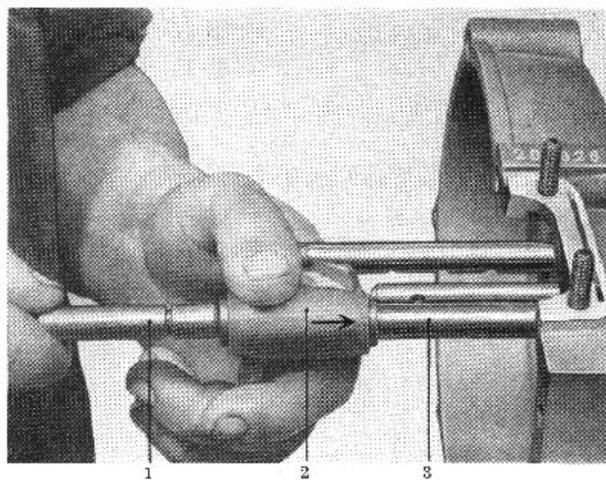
Schaltgabel mit Kugel und Druckfeder auf einen gebrauchten Schaltbolzen aufschieben
